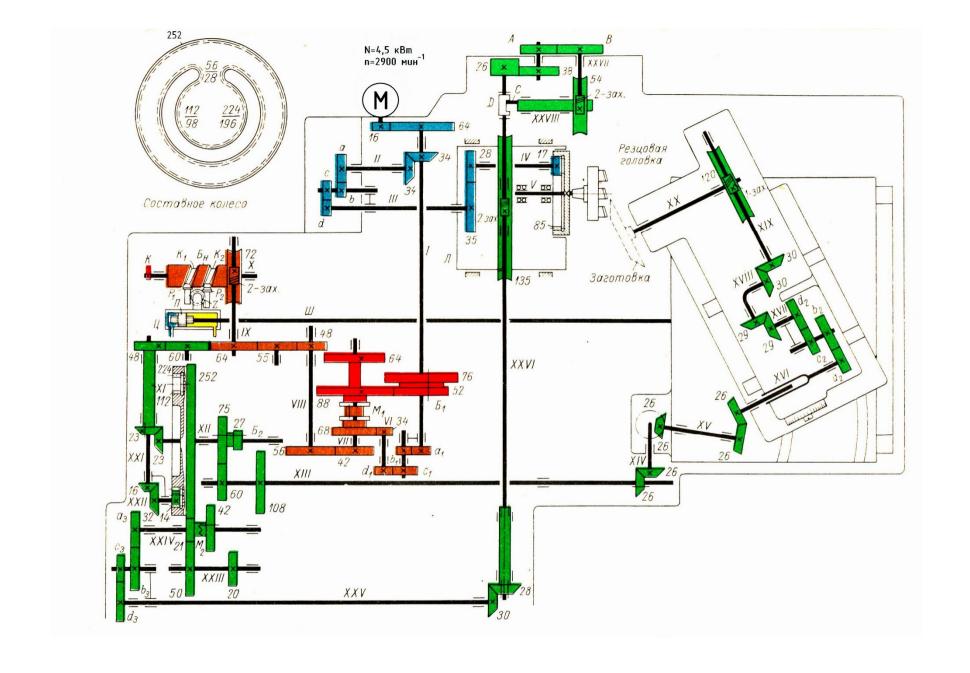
Кинематическая схема зуборезного полуавтомата для конических колёс модели 525
